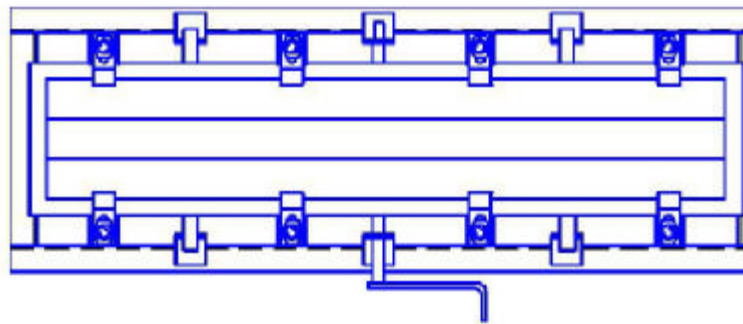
Схема пристосування для наплавлення робочої поверхні ножа відвала
